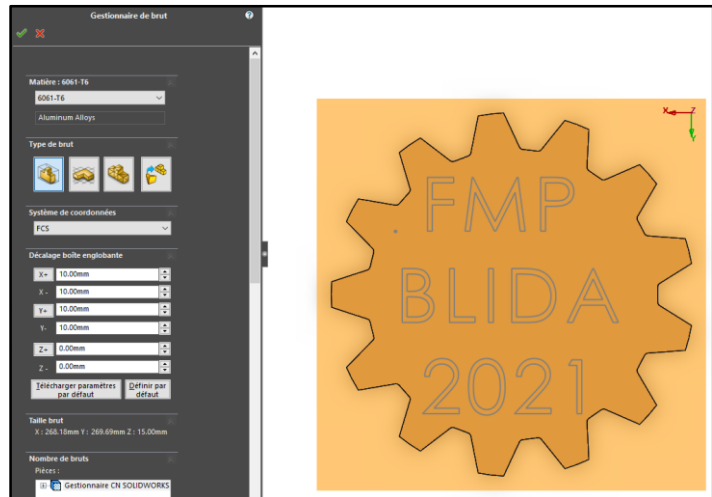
28 : Définitions de l'origine et les dimensions de la pièce brute
